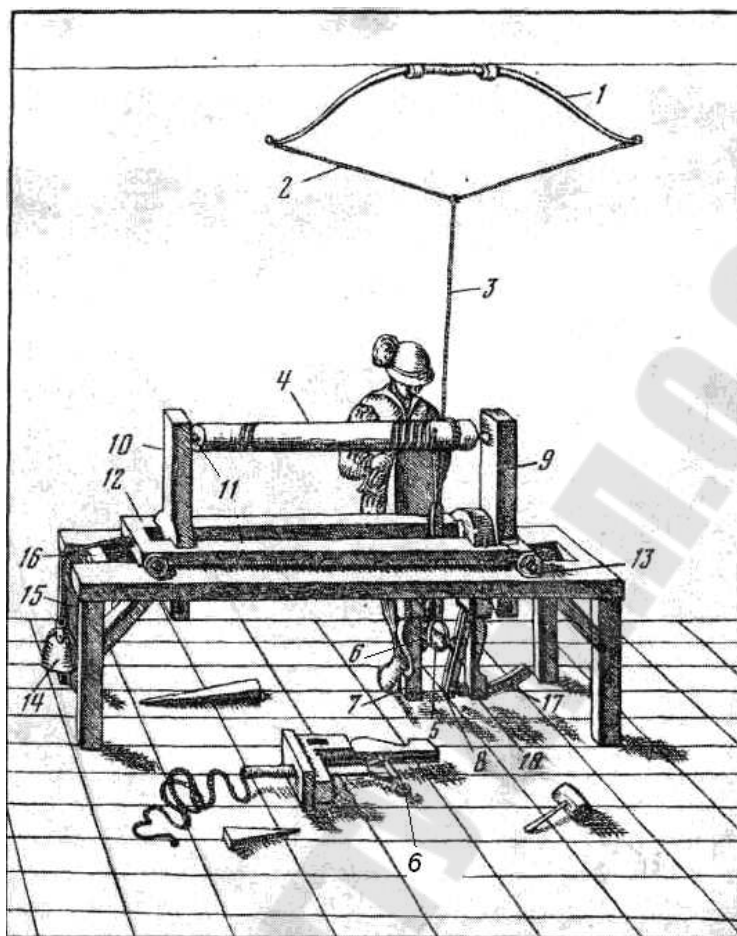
Эскиз токарно-винторезного станка (по Жану Эрару 1584г.):
